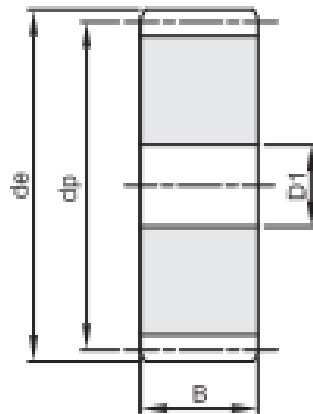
Principales dimensiones de los engranajes seleccionados. *Fuente: www.beatransmision.com
